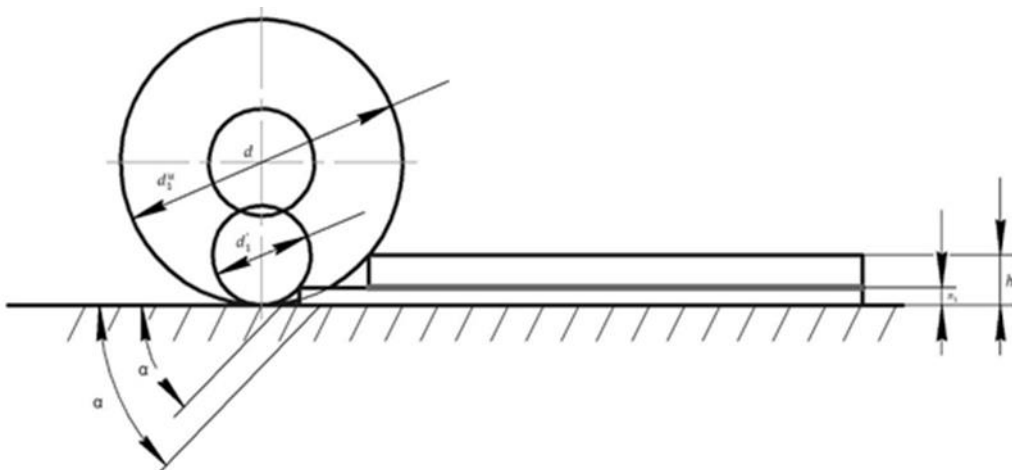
Схема влияния диаметра пневматической шины на толщину захватываемой и подаваемой заготовки
